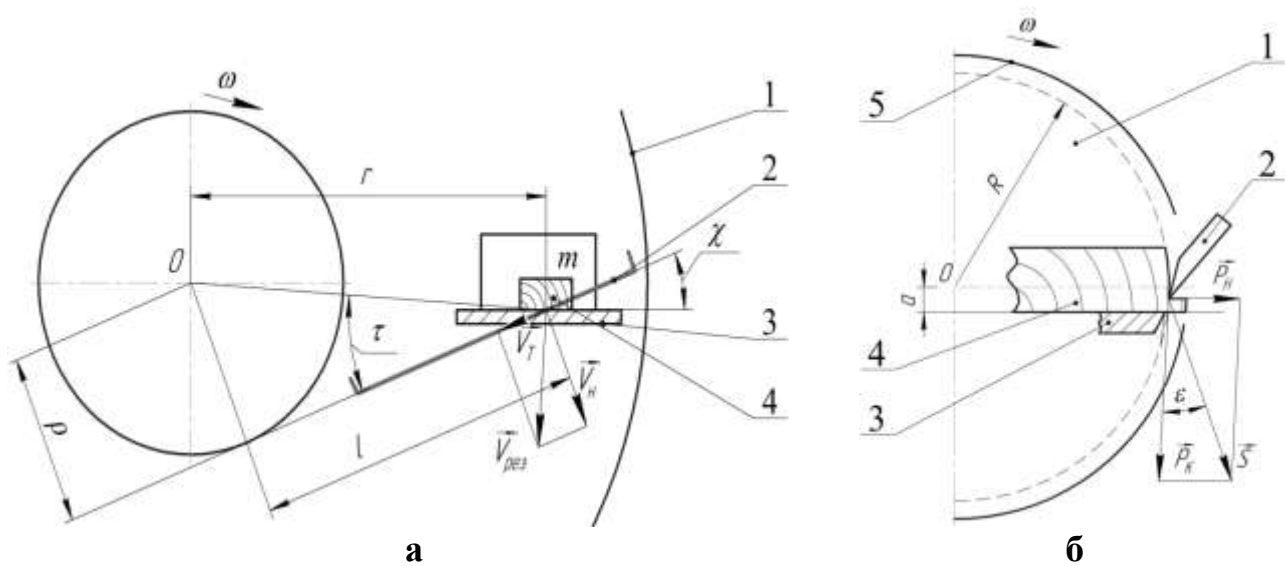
Схемы режущих аппаратов: а – дискового; б – барабанного: 1-диск; 2 – нож; 3 – противорезущая пластина; 4 – материал; 5 – барабан
